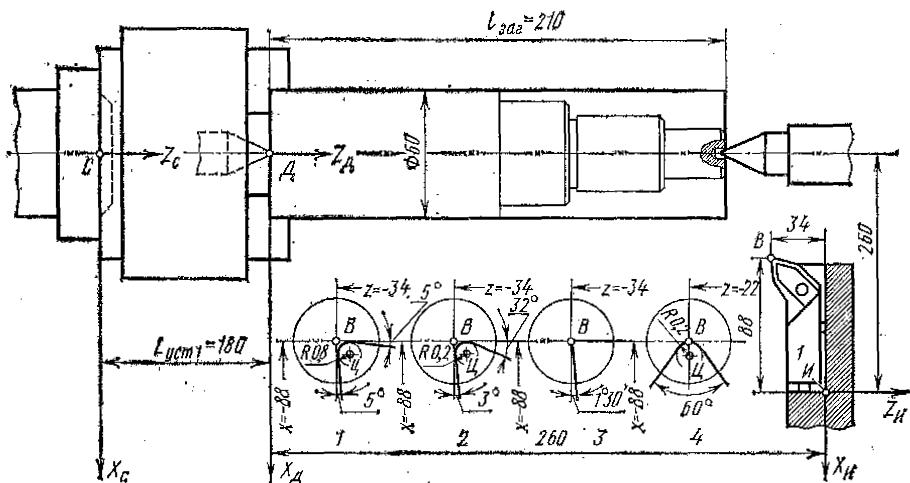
Операционный эскиз токарной обработки детали «вал»
